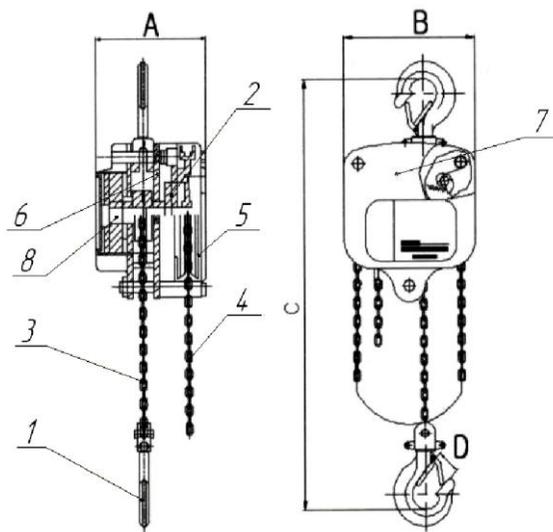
Устройство тали ручной цепной HS-Z – 622-A.
